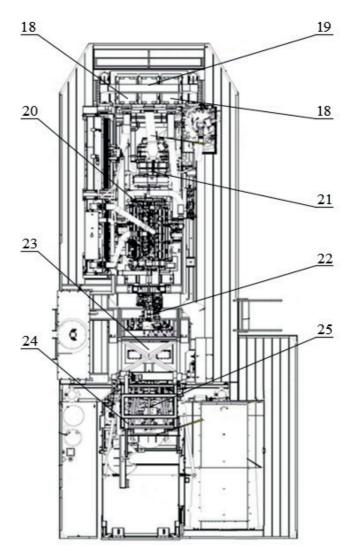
Основные узлы и механизмы буровой установки (продолжение): 18 – воздухоочистители двигателя; 19 – воздухоочиститель; 20 – двигатель платформы; 21 – компрессор; 22 – гидравлические насосы и редуктор; 23 – гидравлический резервуар; 24 – деррик-кран, ведущий механизм, вышка (вертикальное положение); 25 – вращающаяся головка
